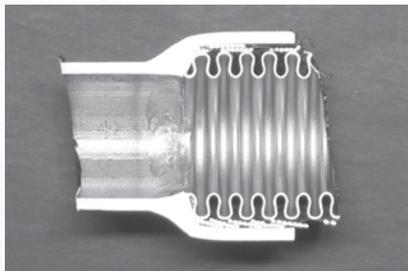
Soudure sur une tuyauterie flexible HYDRA
